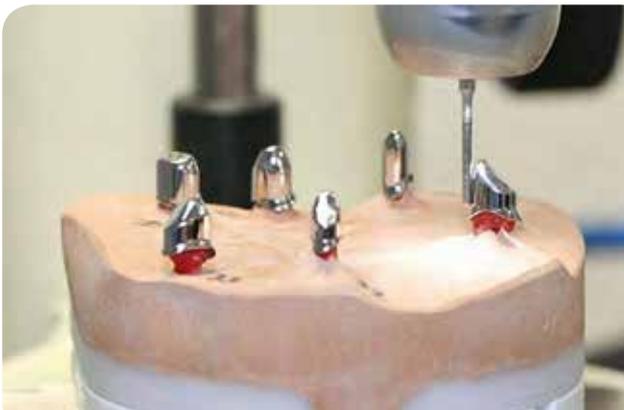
Ein exaktes Fräsen der Primärteile ist besonders wichtig.
